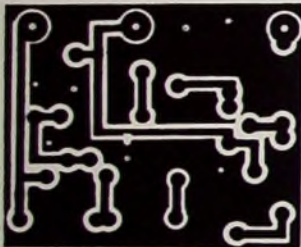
Leiterplatte für die Schaltstufe (Maßstab 1:1)
